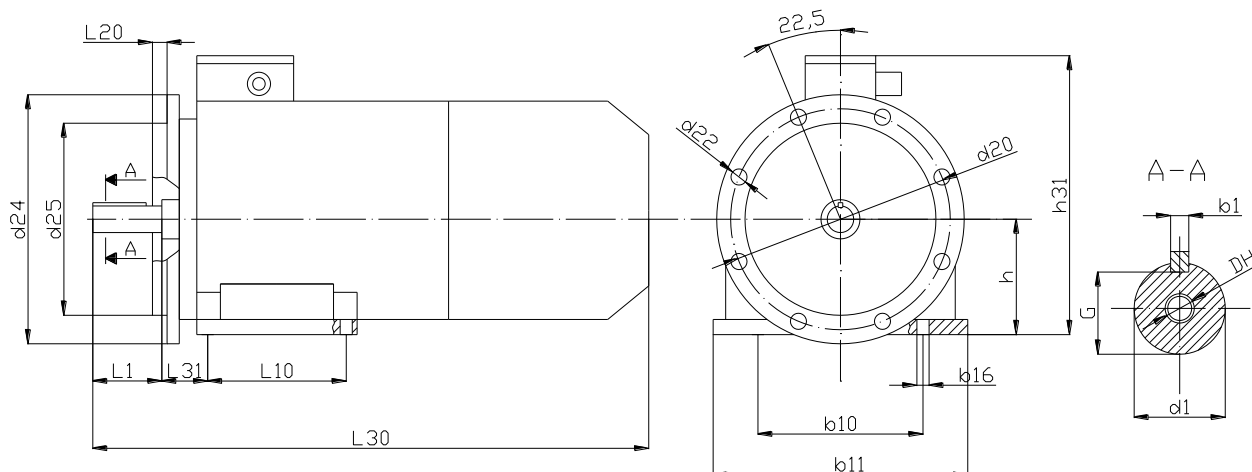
Габаритные и установочно-присоединительные размеры
